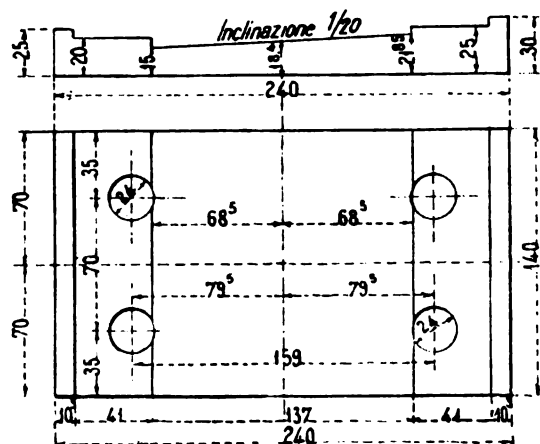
e 7. — Piastra d'appoggio. — Elevazione e pianta.
